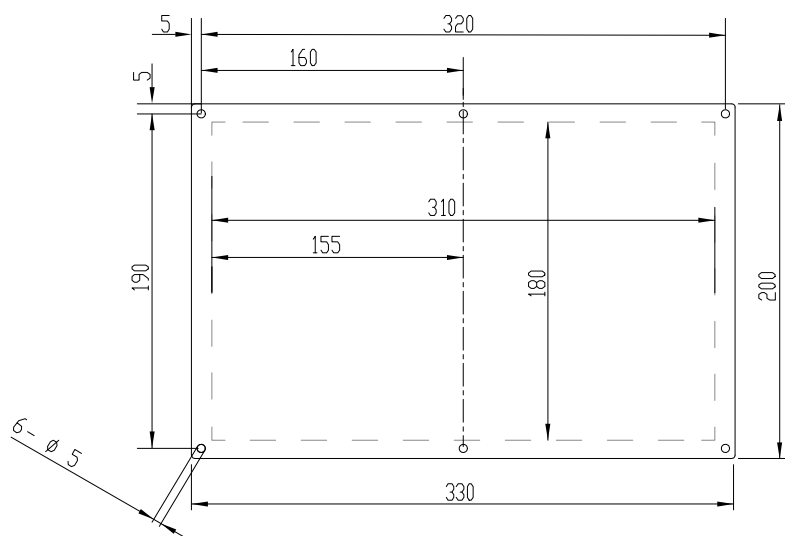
Рекомендуемый монтажный чертеж размеров отверстия для шкафа из листового металла – нижняя панель цельного контроллера N5
